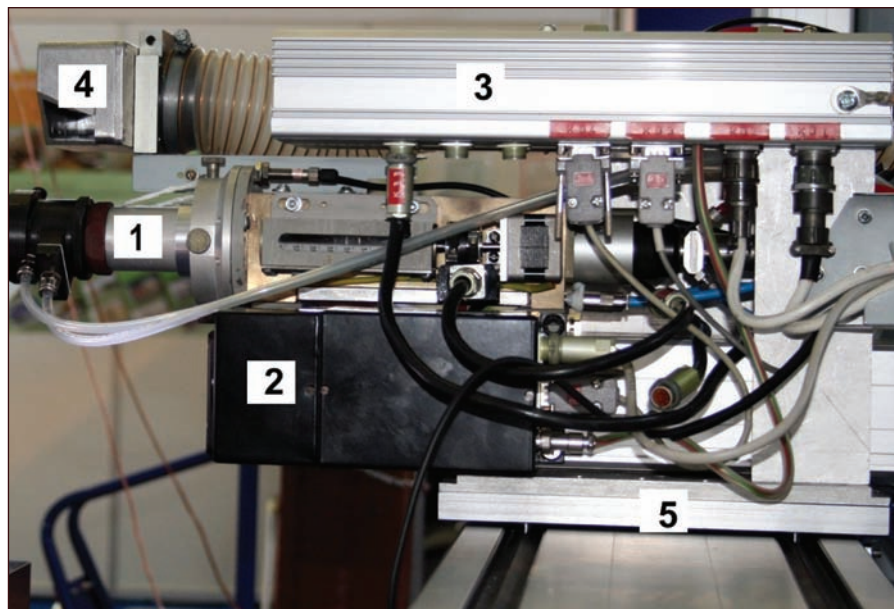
Сварочная головка в составе сварочного комплекса
